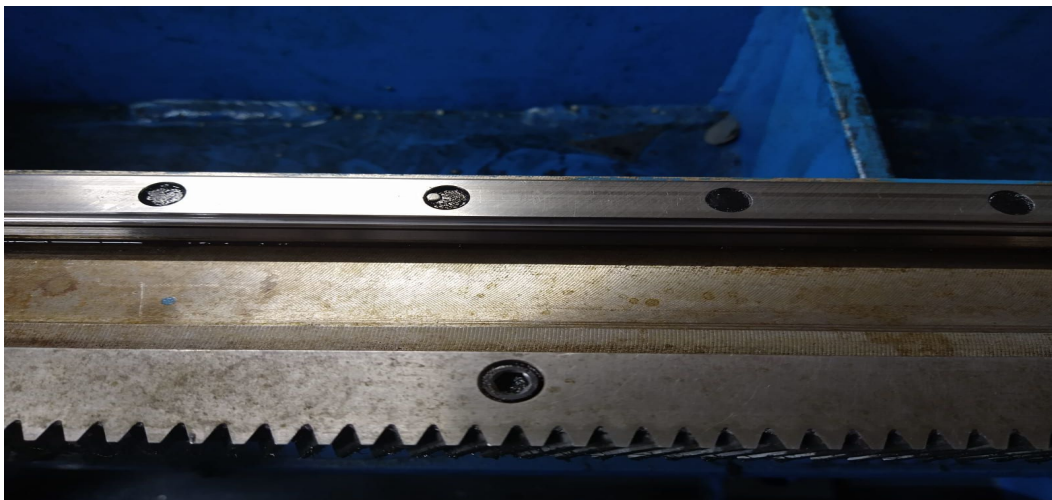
Guía y cremallera aplicando el plan de lubricación
